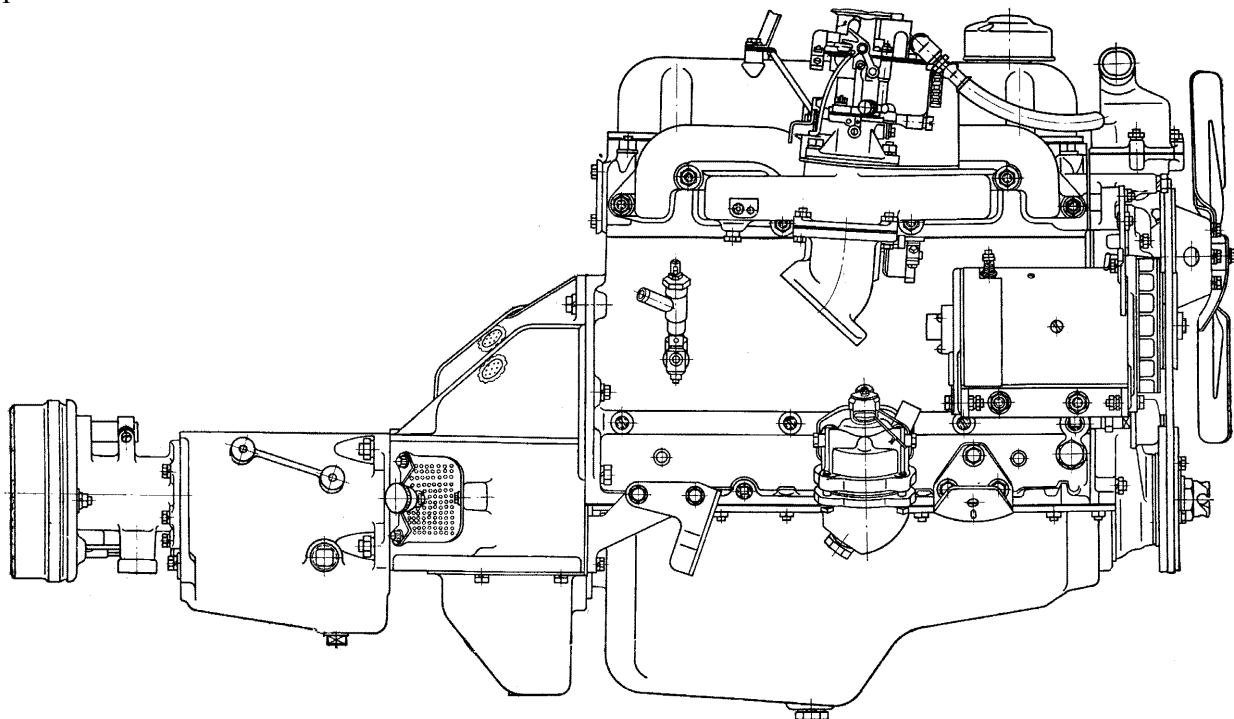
Двигатель со сцеплением и коробкой передач (вид справа)
